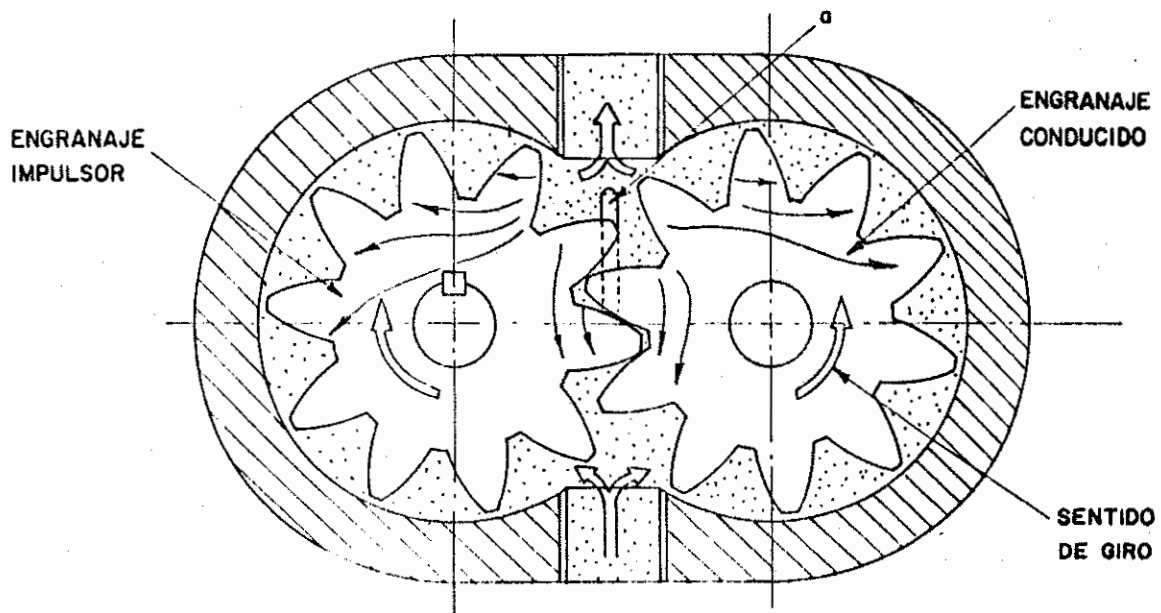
Bomba de engranajes de piñones iguales, dentado recto y exterior.
